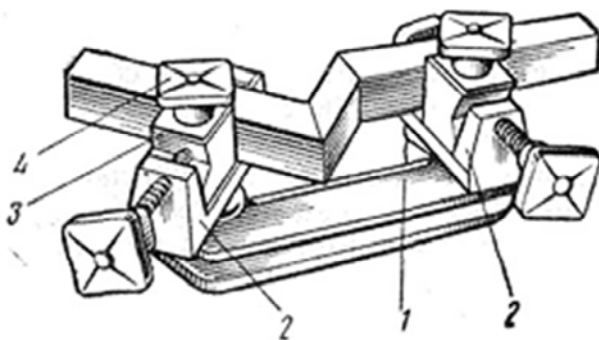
Универсальное приспособление для сварки мелких узлов: 1 – платформа; 2 – струбцины; 3 – призма; 4 – винт-фиксатор
